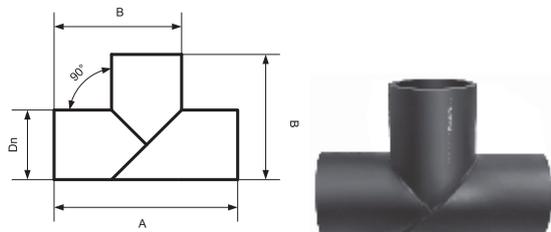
Тройник 90° сварной равнопроходной.
